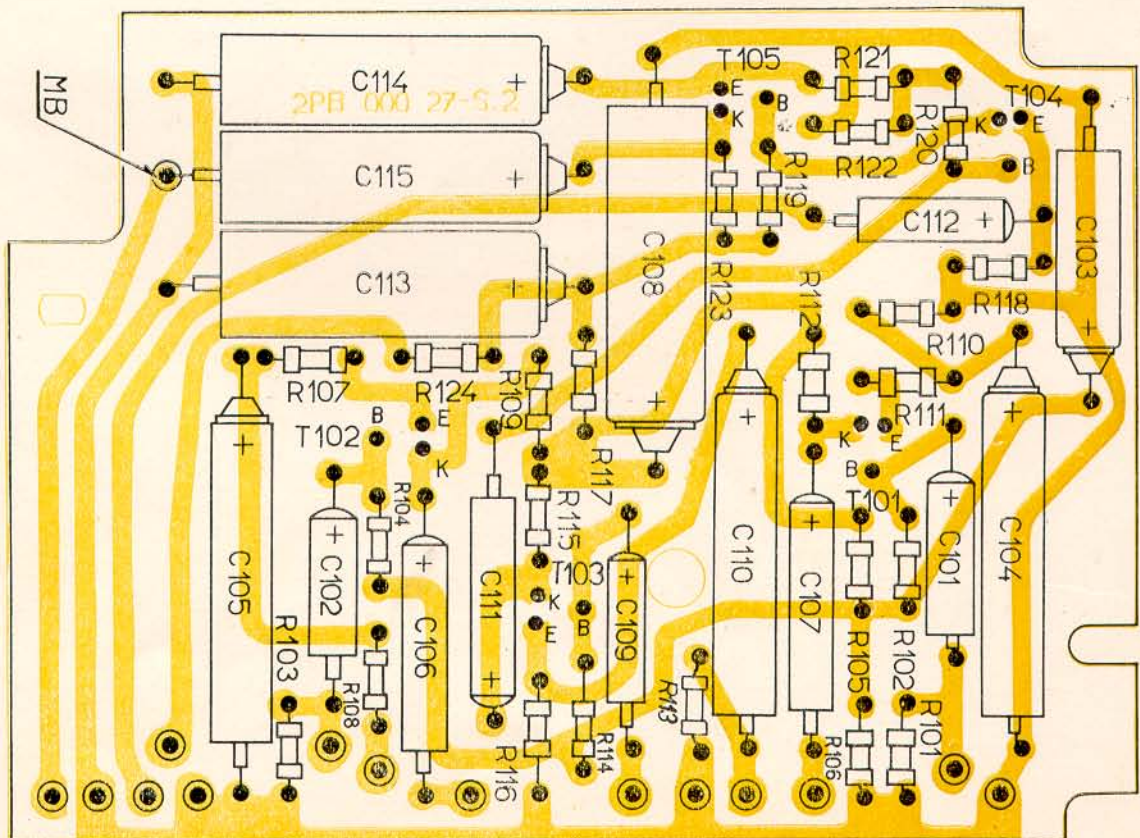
KONCOVÝ ZESILOVAČ (pohled ze strany spojů)
